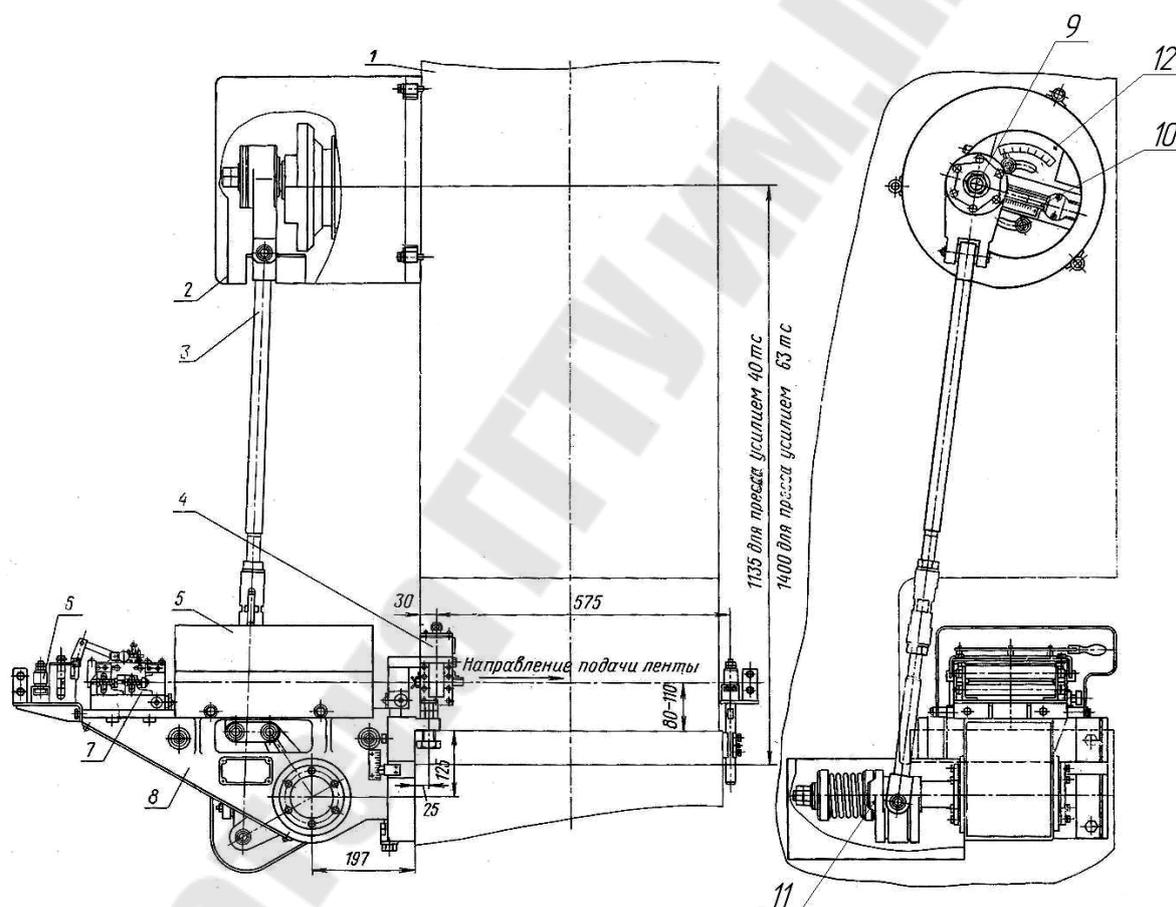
Общий вид модели РКП11: 1- пресс, 2 - ограждение привода, 3 - привод, 4 - устройство для смазки ленты, 5 - ограждение, 6 - устройство для очистки ленты, 7 - каретка, 8 - привод каретки, 9 - палец, 10 - регулировочный винт, 11 - муфта предохранительная, 12- планшайба
